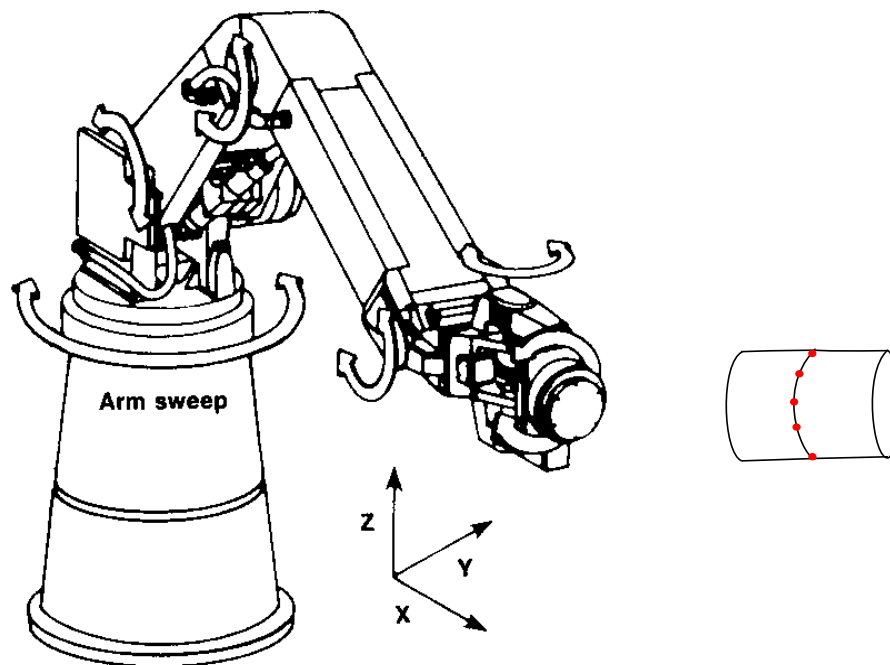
Caso de robot soldador en superficie tubular.
